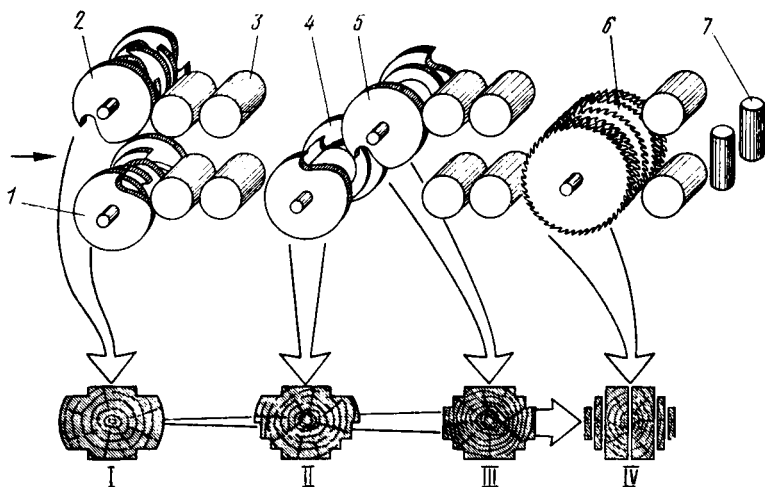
Принципиальная схема работы фрезерно-пильного агрегата: 1 - нижняя головка узла первичного фрезерования, 2 - верхняя головка узла первичного фрезерования, 3, 7 - подающие вальцы, 4 - нижняя головка узла вторичного фрезерования, 5 - верхняя головка узла вторичного фрезерования, 6 - пильный узел
